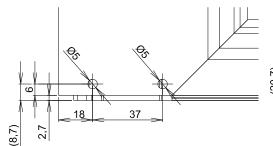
Positionierbohrungen Mitteldichtblock M432 seitlich
